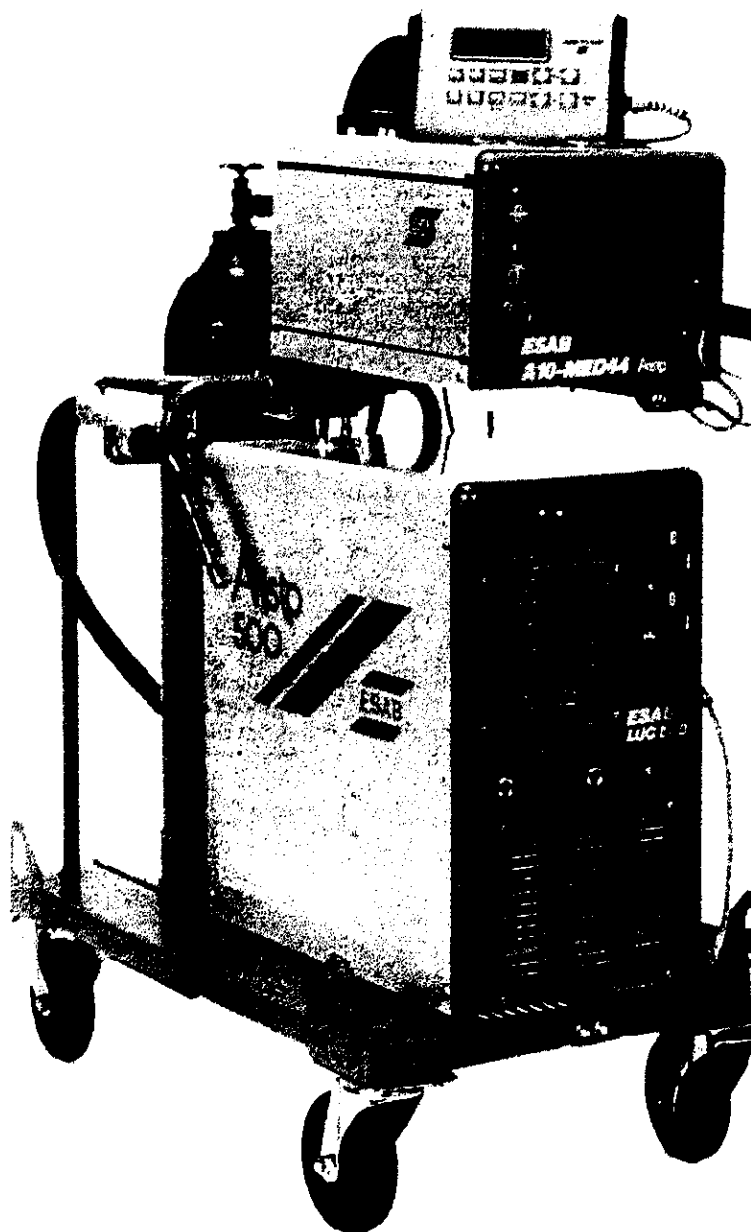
Equipo de soldadura ARISTO 500.
